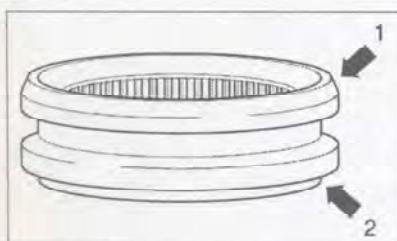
Установка скользящей муфты синхронизатора 1-й/2-й передач.
